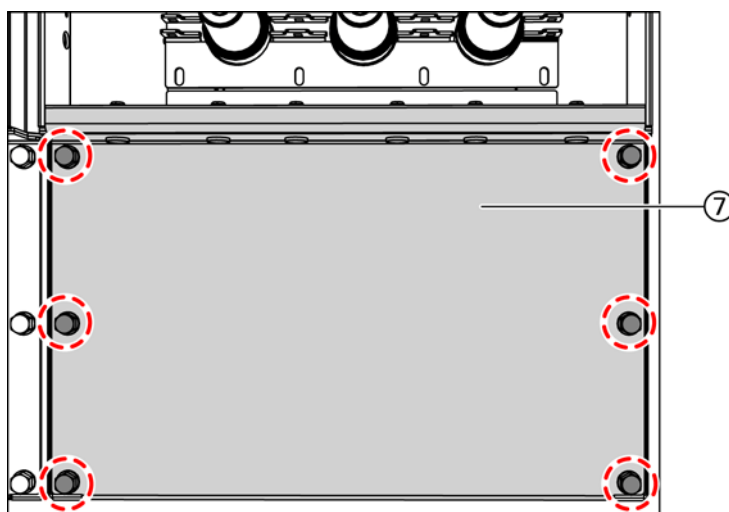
Монтаж поперечной стенки (Т-ячейка)
